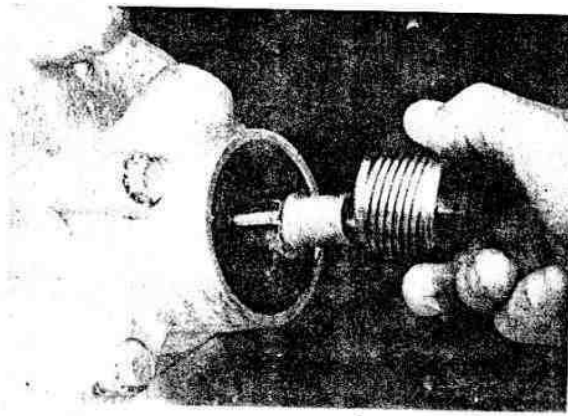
Instalando el engranaje sinfín del velocímetro.
